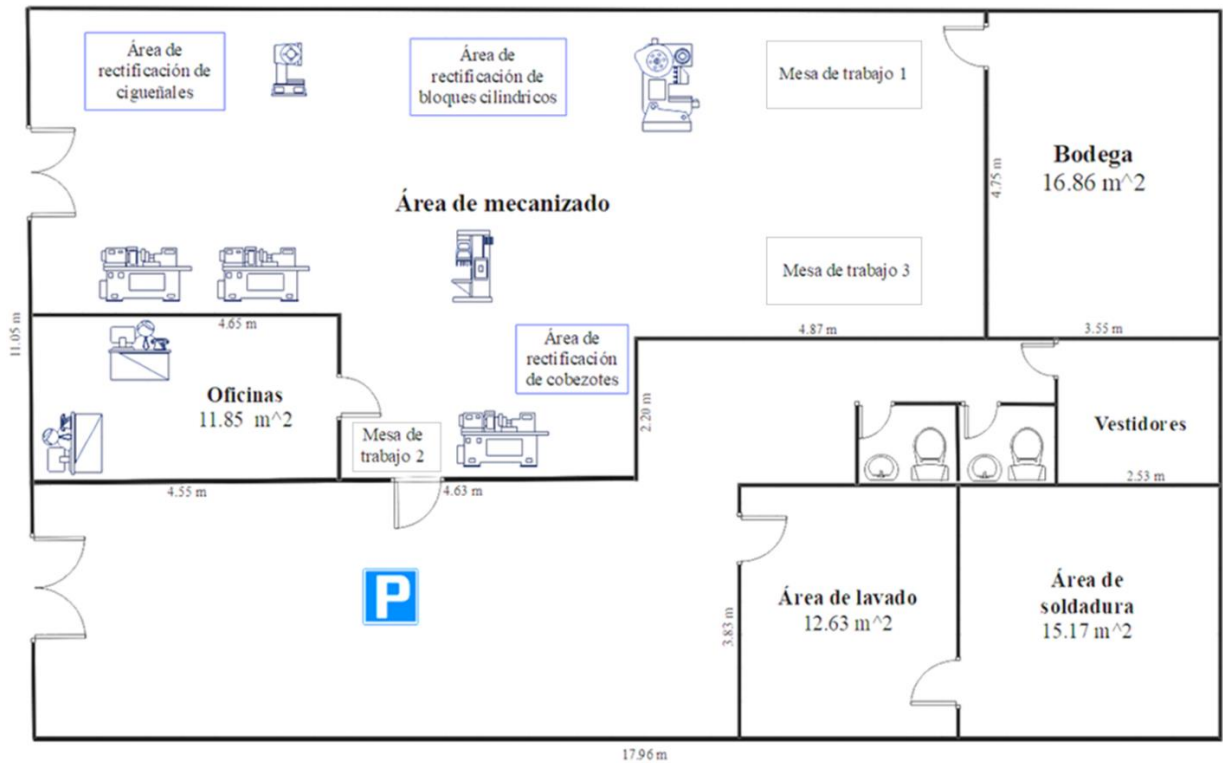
Layout de la planta de la empresa Rectificadora Cotopaxi.
